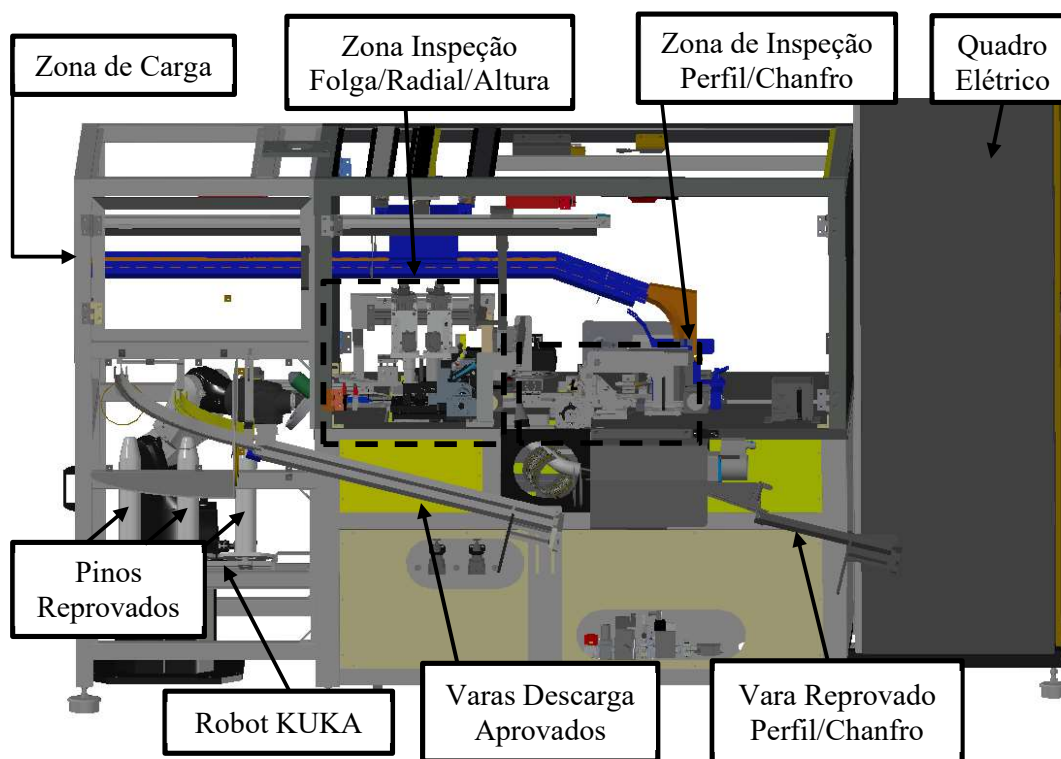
Zonas Máquina de Inspeção Dimensional
